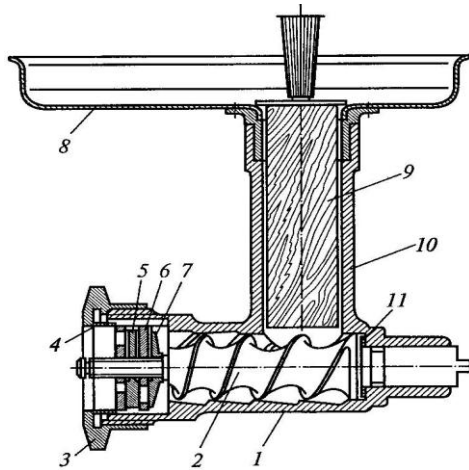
Мясорубка МКМ-82 к универсальному приводу: 1 – корпус; 2 – шнек; 3 – нажимная гайка; 4 – упорное кольцо; 5, 6, 7 – режущий инструмент; 8 – загрузочная чаша; 9 – толкатель; 10 – горловина мясорубки; 11 – шайба
